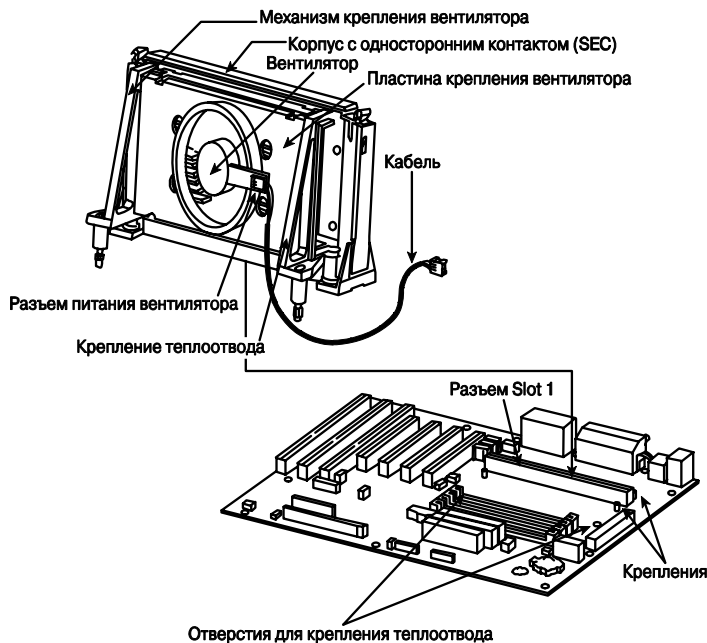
Процессор Pentium II/III и крепление радиатора
